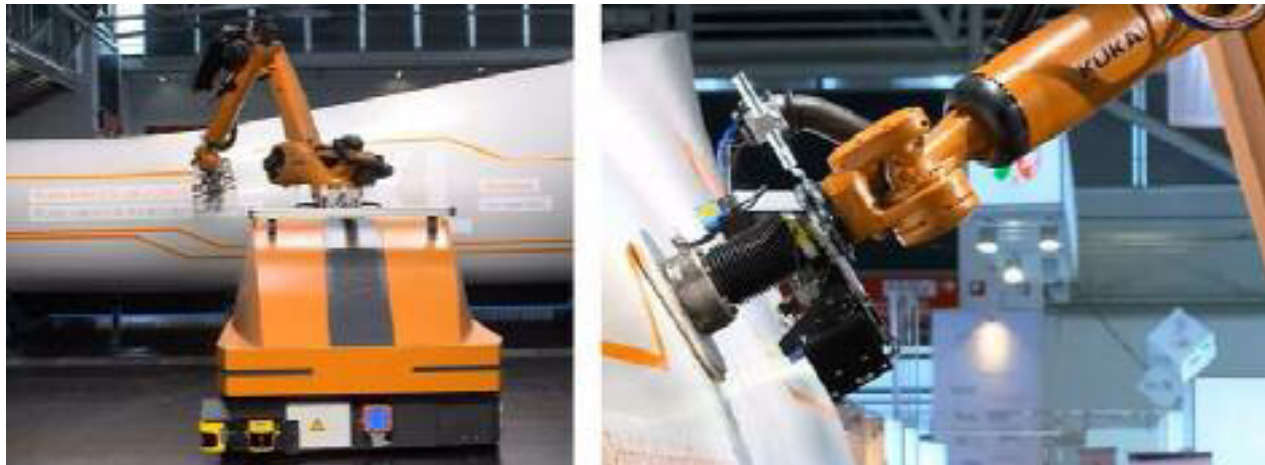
Використання мобільного робота KUKA moiros для обробки поверхні
